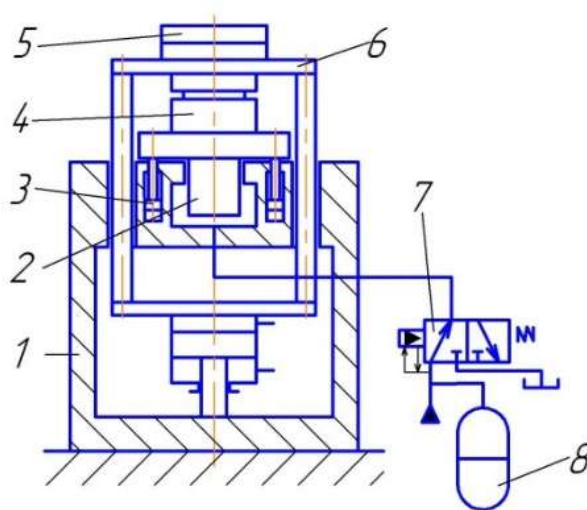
Інерційний прес (ІП): 1 – станина; 2. – нижній стіл; 3. – пружний зворотний елемент; 4. – корпус; 5. – нерухома змінна інерційна
